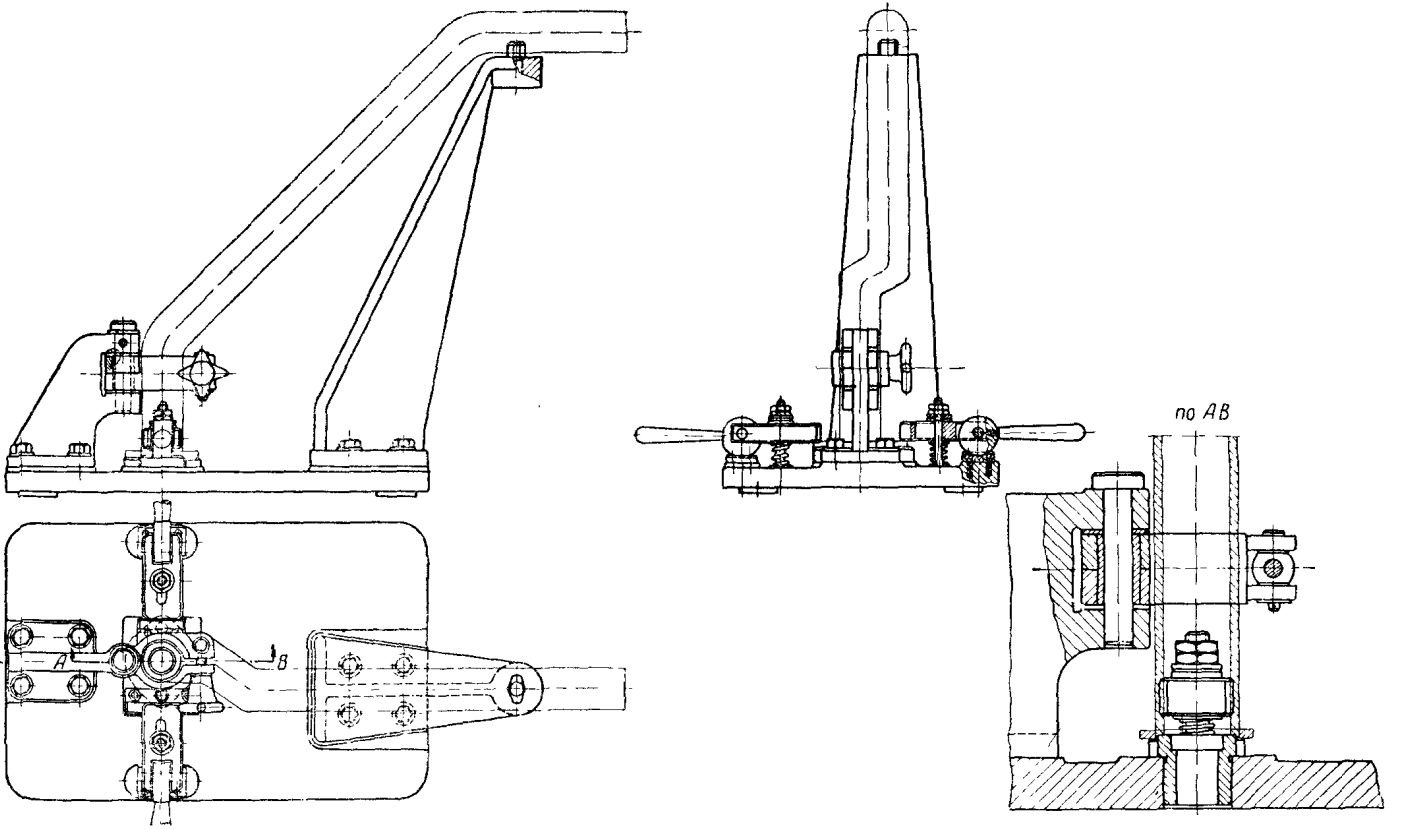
Приспособление с эксцентриковыми прижимами для сборки трубчатого узла.
